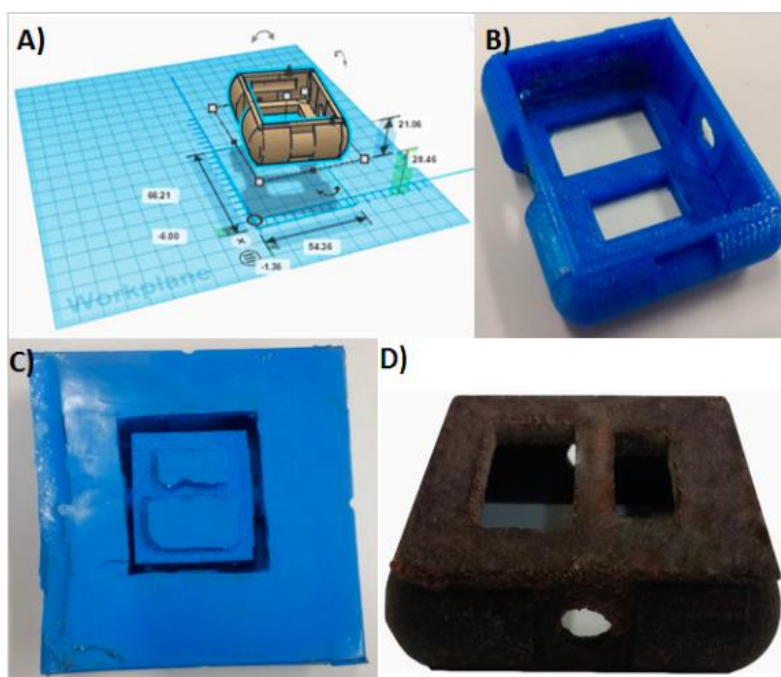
(A) Molde tridimensional; (B) impressão 3 D; (C) Molde de silicone e (D) Carcaça do relógio inteligente
